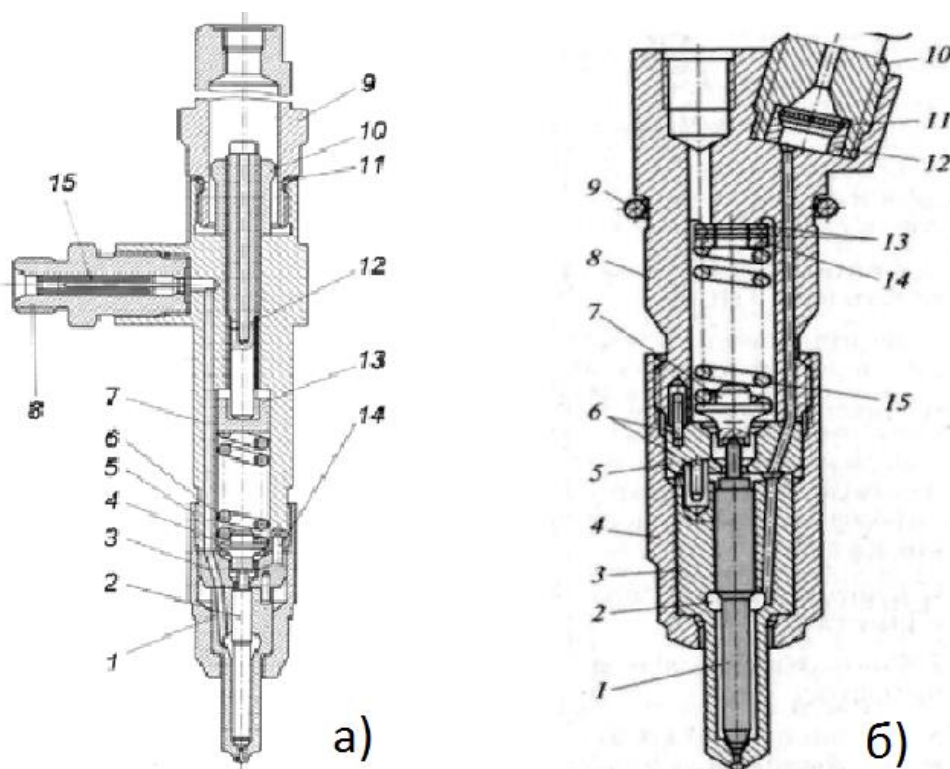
Устройство форсунок: а – ЯМЗ: 1 – корпус распылителя; 2 – игла распылителя; 3 – проставка; 4 – штанга; 5 – гайка распылителя; 6 – пружина; 7 – корпус; 8 – штуцер с фильтром; 9 – колпак; 10 – гайка; 11 – шайба; 12 – регулировочный винт; 13 – тарелка пружины; 14 – штифт; 15 – щелевой фильтр;
